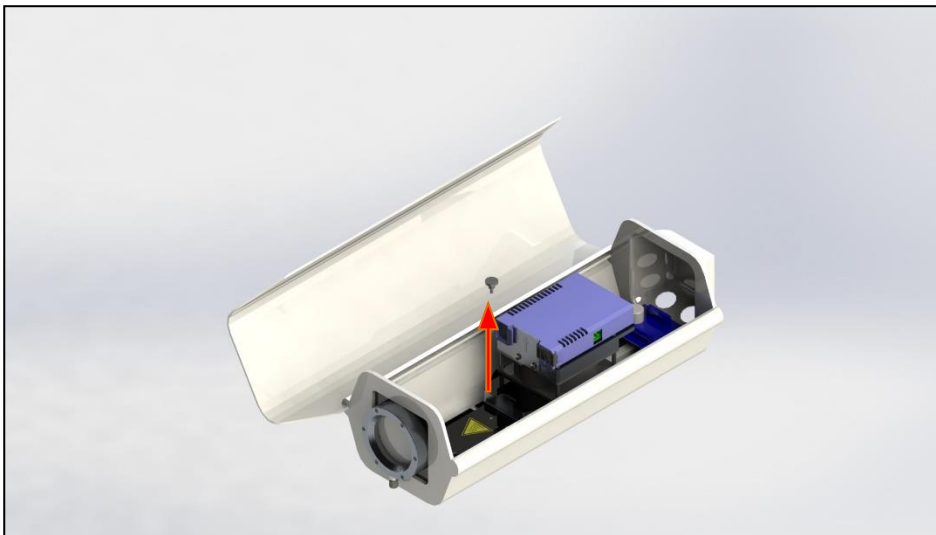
Lösen der Rändelschraube vom Befestigungsblech
